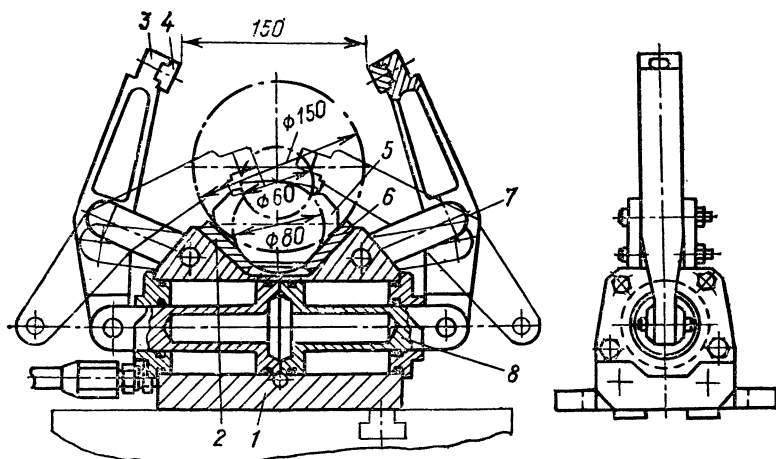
Специализированное наладочное приспособление для фрезерования деталей типа валов и втулок
